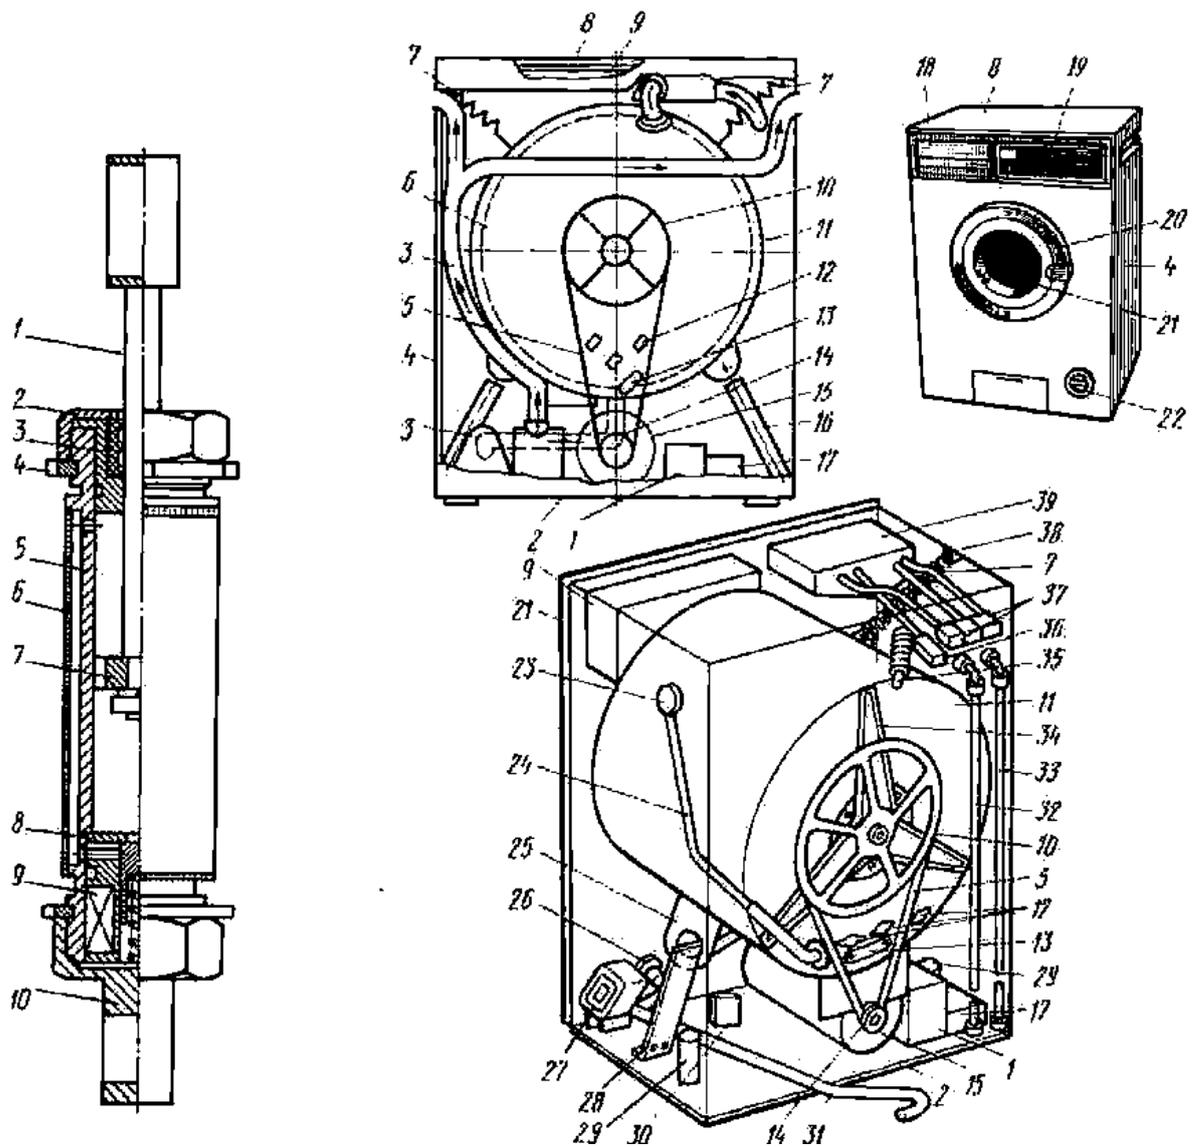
Амортизатор: 1- шток; 2 - гайка; 3 - втулка; 4 - контргайка; 5 - внутренний цилиндр; 6 - наружный цилиндр; 7 - поршень; 8 - шайба; 9 - катушка; 10 - гайка
